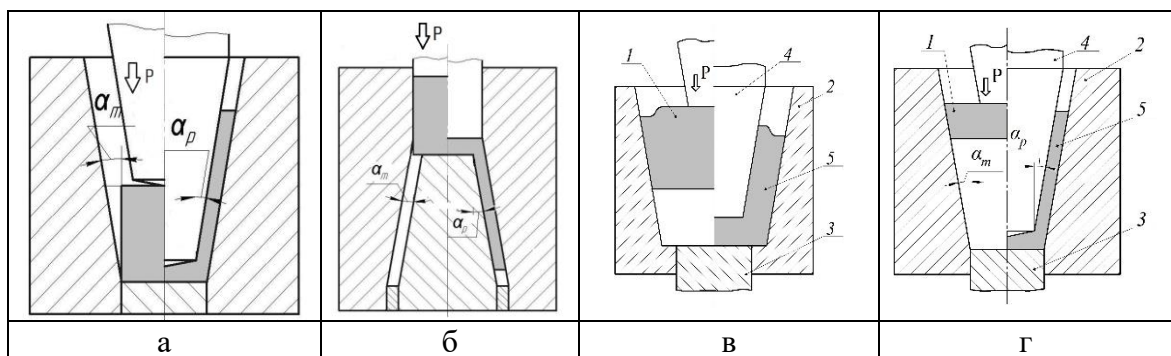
Схеми видавлювання порожнистих деталей типу «конічний стакан»
